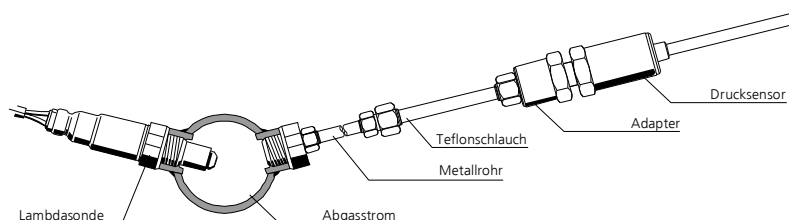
Thermisch entkoppelte Montage des Drucksensors
